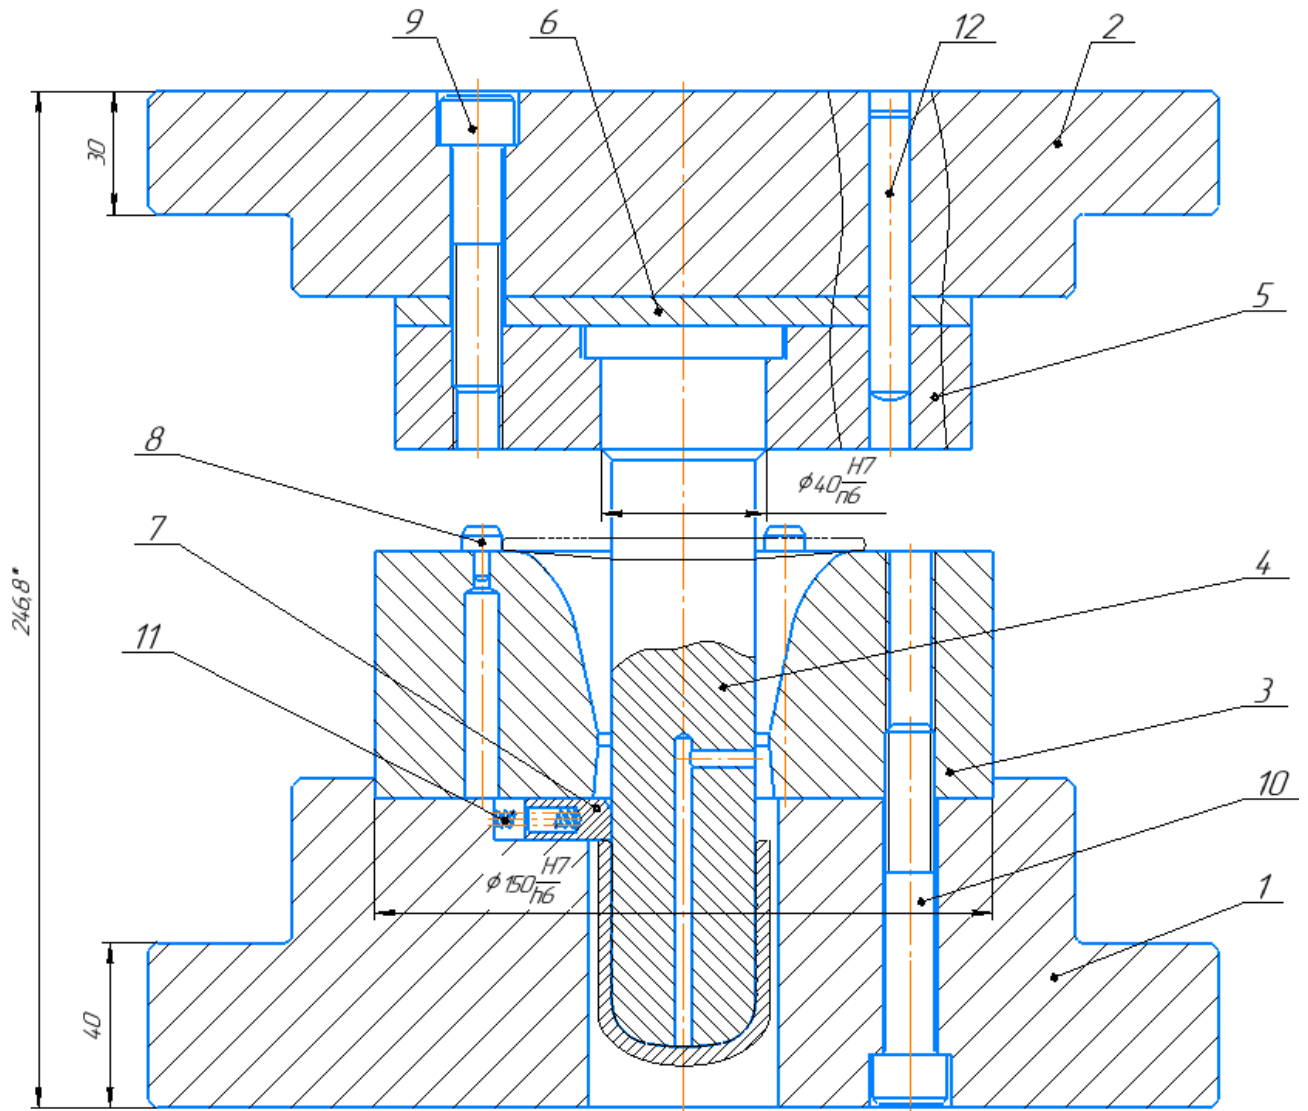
Загальний вигляд штапу для витягування у
